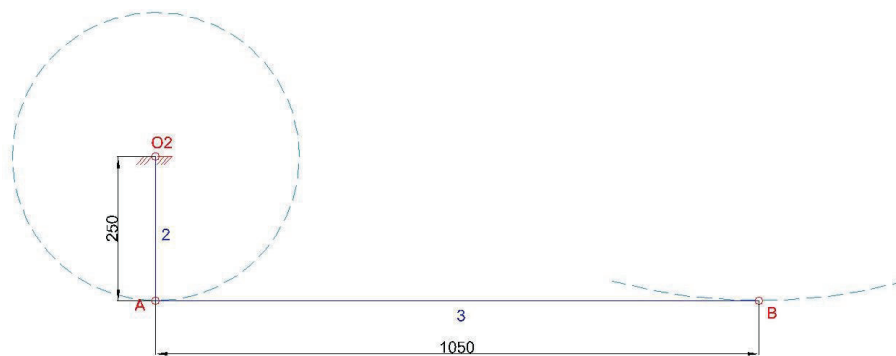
Dimensiones de los eslabones manivela y biela acopladora.
